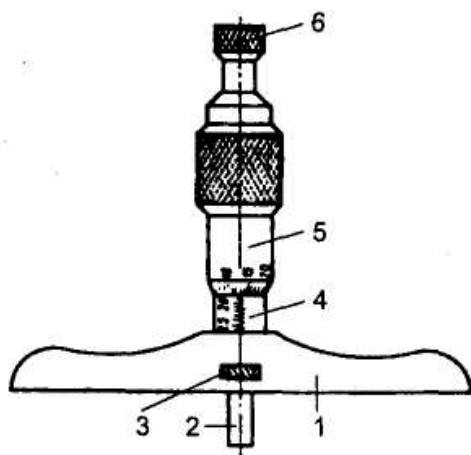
Микрометрический глубиномер: 1 - корпус;
